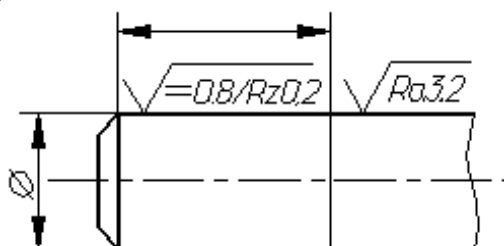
Пример обозначения различной шероховатости на одной поверхности
